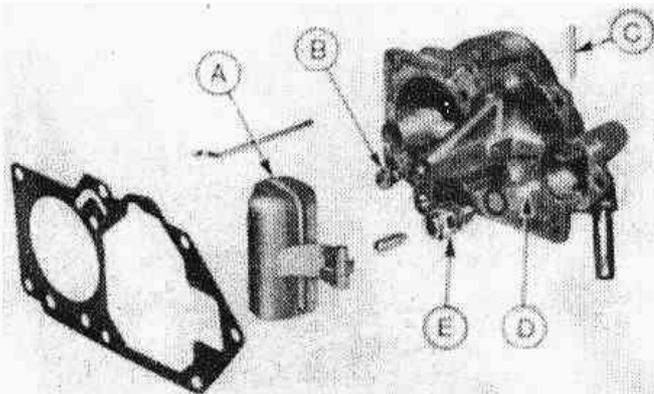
Поплавок (А), жиклер главной дозирующей системы (В), крепежная шпилька (С), топливный фильтр (D), крышка клапана (E) (Разд. 22)
